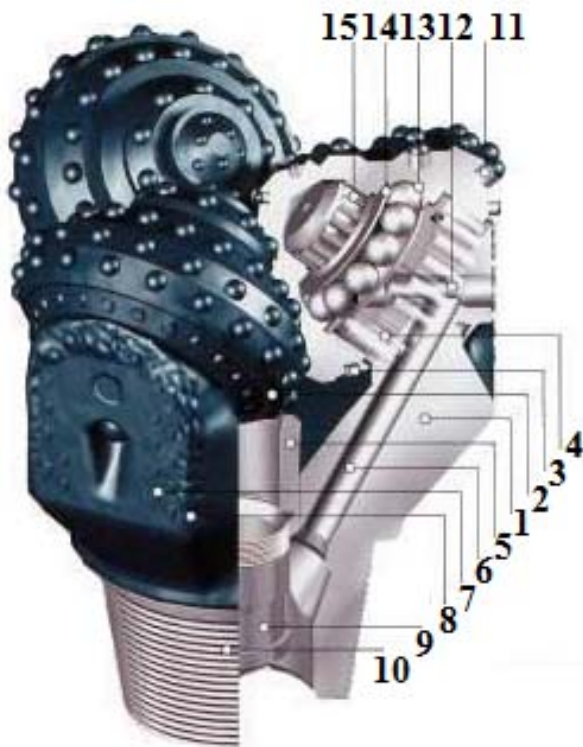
Вигляд шарошкового долота: 1 – лапа; 2 – шарошка; 3 – захісні зубці; 4 – роликовий підшипник; 5 – сопло; 6 – продувний канал; 7 – бокові захісні зубці; 8 – наплавлений шар; 9 – зворотний клапан; 10 – різь; 11 – твердосплавні зубці; 12 – замок; 13 – замковий підшипник; 14 – упорний підшипник ковзання; 15 – кінцевий роликовий підшипник
